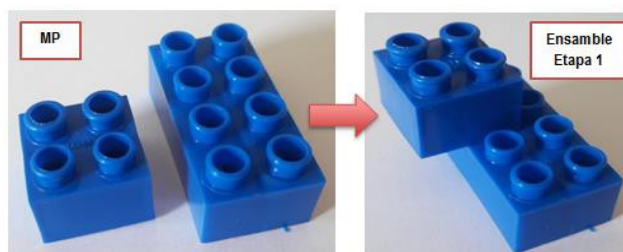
Sub producto de la primera etapa de montaje del diseño de experimento – Fuente: Elaboración propia.
